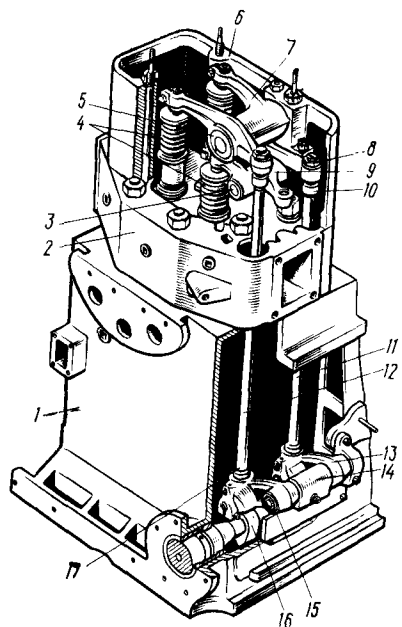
Привод клапанов крышки цилиндра дизеля ПД1М:
